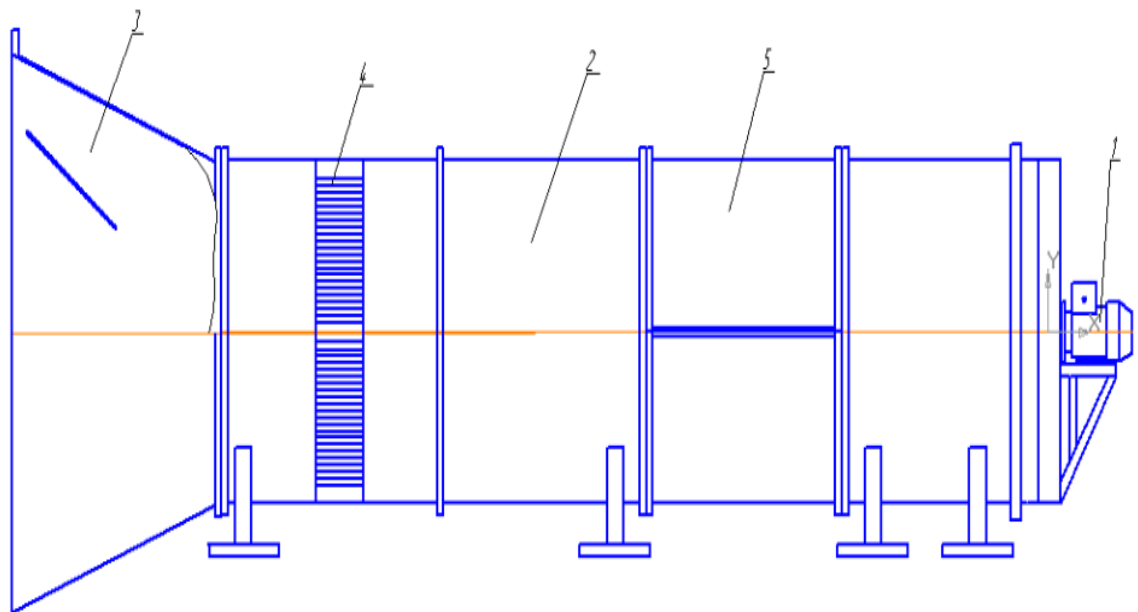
Конструктивна схема аеродинамічної труби
